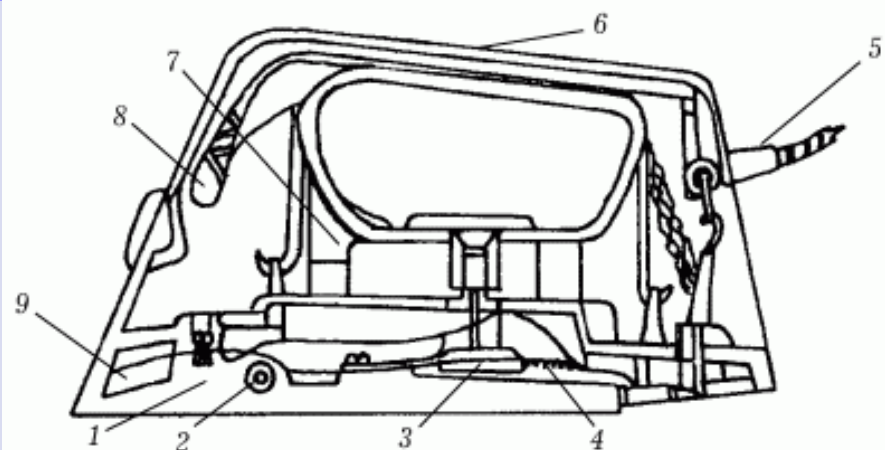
Устройство электрического утюга марки УТ: 1 – подошва; 2 – трубчатый электронагреватель (ТЭН); 3 – терморегулятор; 4 – теплоизолирующая прокладка; 5 – шнур; 6 – крышка корпуса; 7 – ручка; 8 – сигнальная лампочка; 9 – кожух корпуса.
